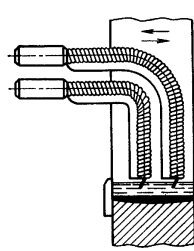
Схема сварки под плавящимся мундштуком
